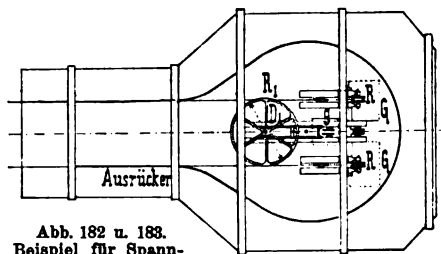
u. 183. Beispiel für Spannvorrichtungen für Trag- und Zugseile. G Spanngewichte für die Tragsseile. R Rollen für die Tragsseile. K Ketten für G und g. g Spanngewicht für das Zugseil. R_1 Scheibe für das Zugseil ($D_1 = 1,5-3$ m Durchm.). F Schlittenartige Führung für R_1 . r Rollen für die Kette K von g.
